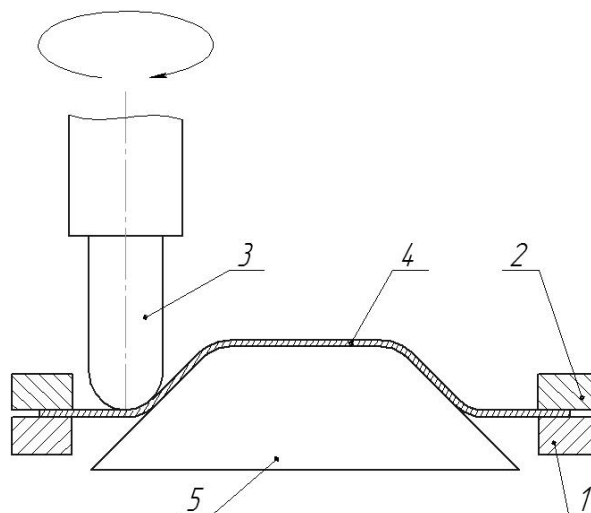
Схема пошарового локального деформування з використанням жорсткого підпору (1 - плита нижня, 2 – плита верхня, 3 – пуансон, 4 – листова заготовка, 5 – жорсткий підпор)
